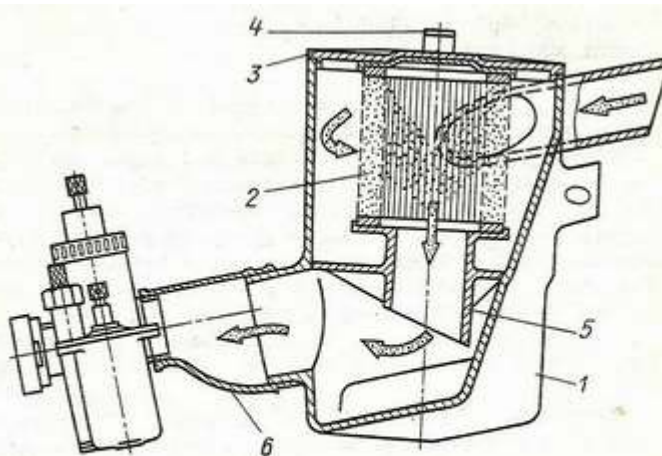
Глушитель шума с фильтрующим элементом для одноцилиндровых двигателей ЯВА-250:
